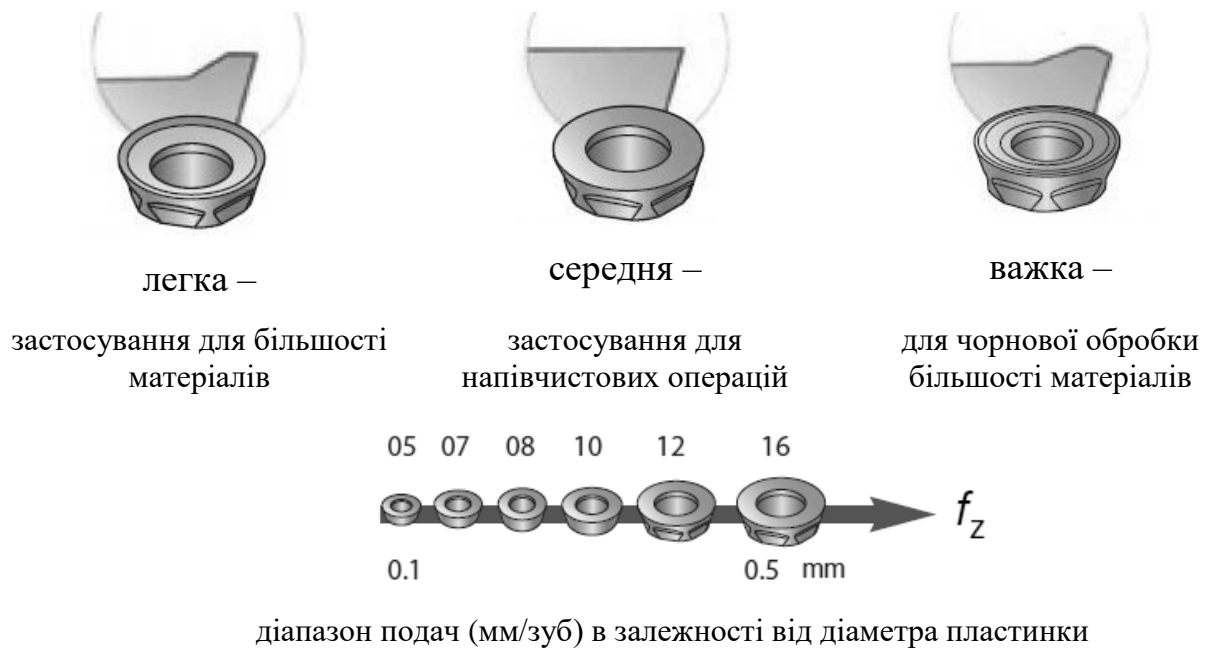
Основні геометрії ріжучих пластин для операцій з низькими зусиллями різання для торцевого фрезерування і обробки профілів та умови їх застосування
